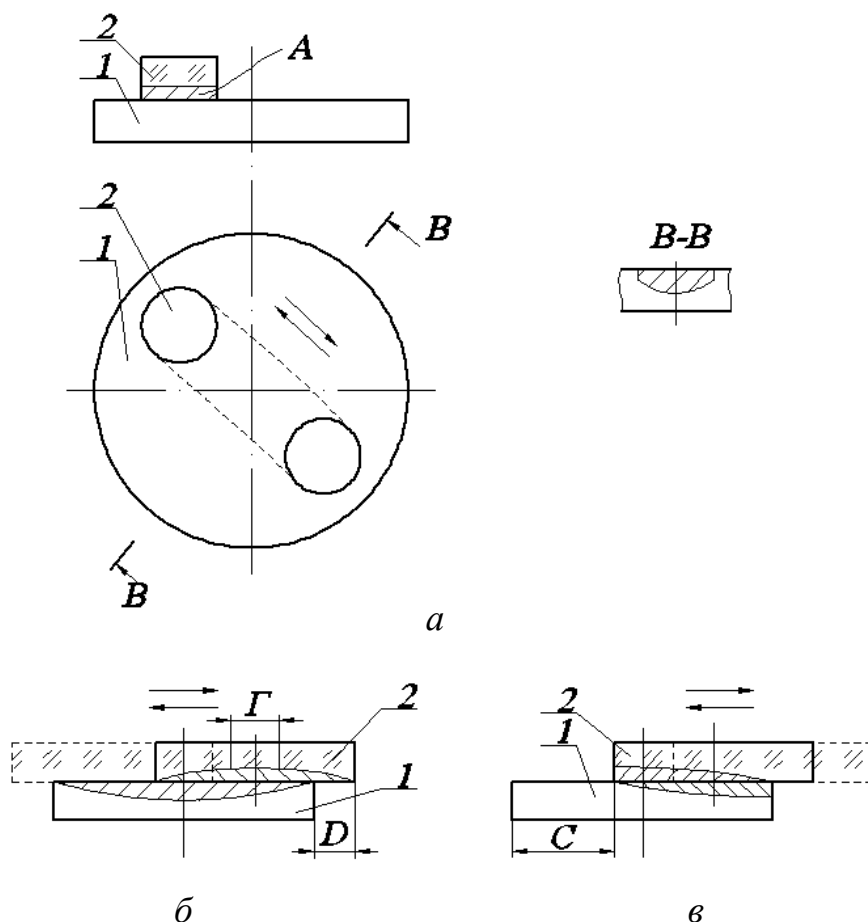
Распределение эюр срабатывания при поступательном перемещении заготовки с плоской поверхностью
